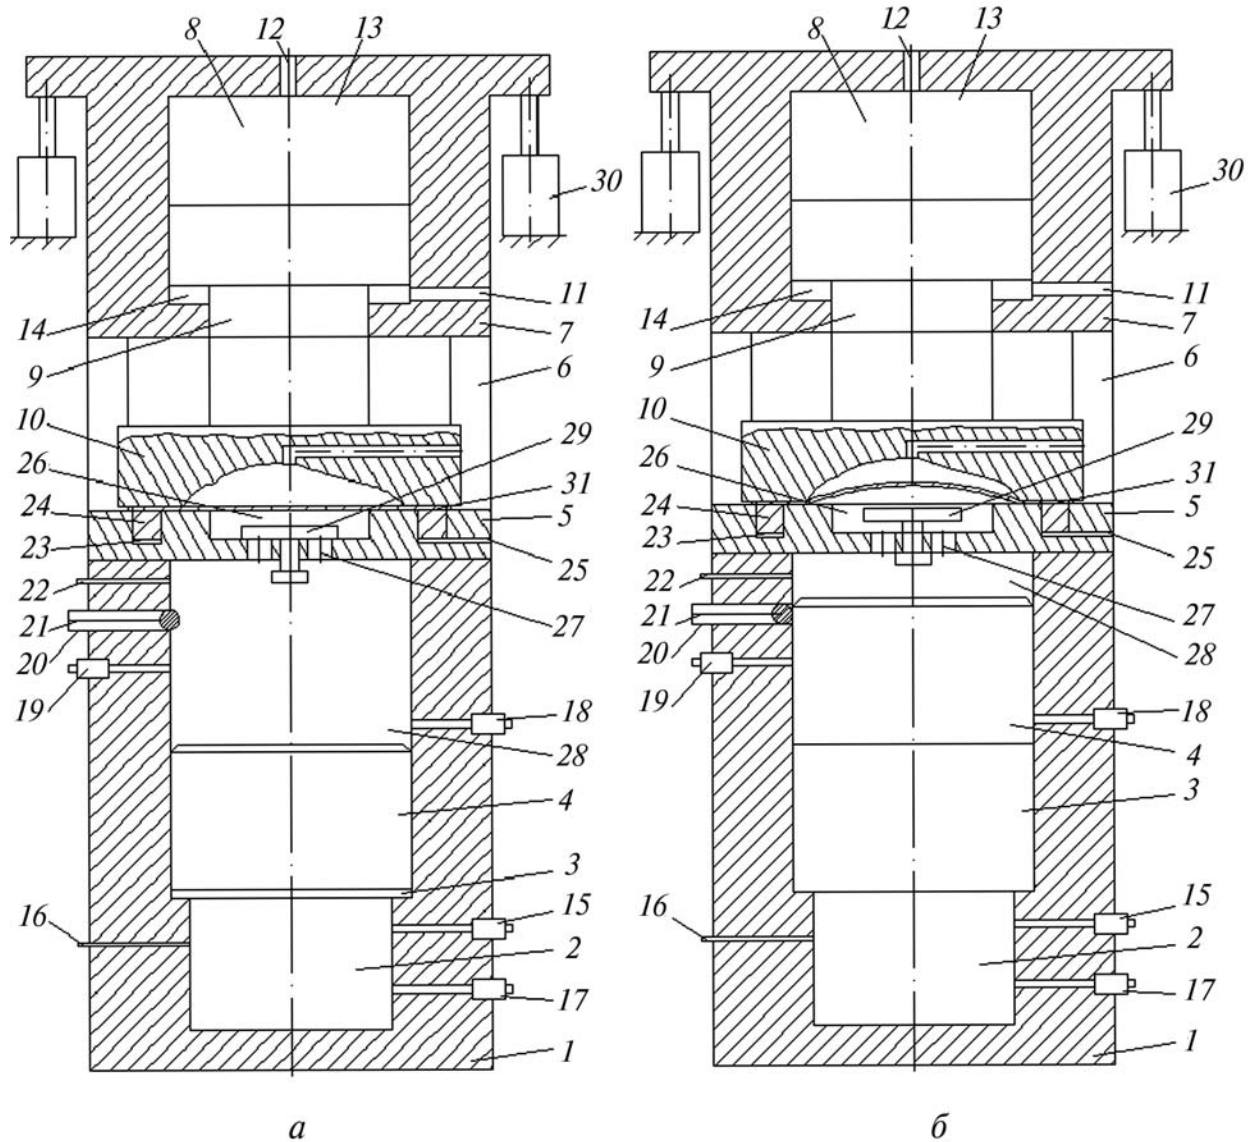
Положения элементов пресса перед началом штамповки (а) и в процесс штамповки (б): обозначения см. на рис. 2
